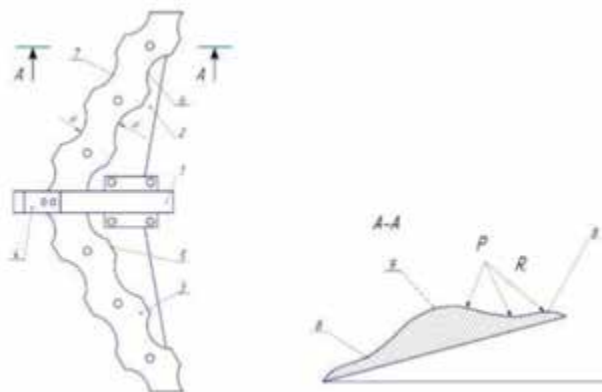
Робочі органи із зубчастими або хвилястими формами робочих поверхонь
